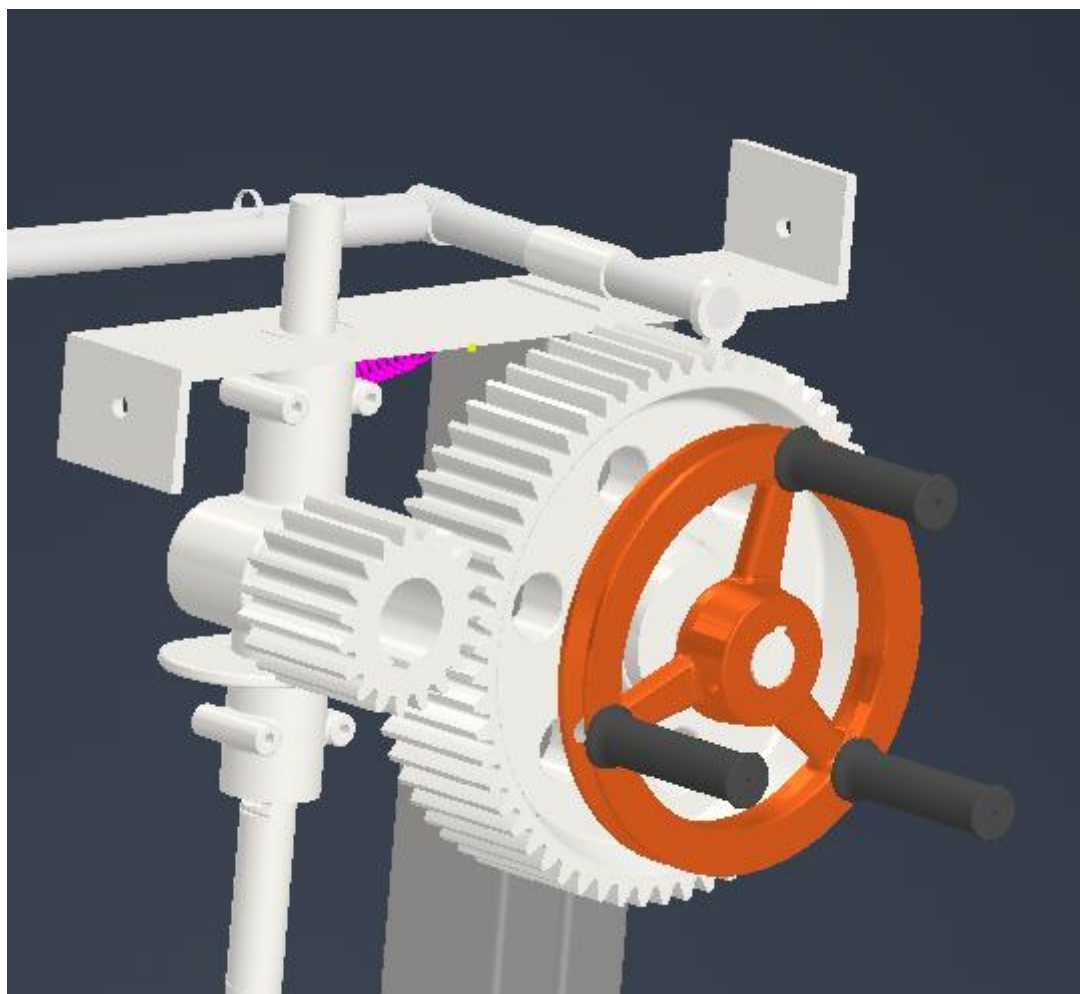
Sistema de engrenagens e setor de direção automotivo adaptado ao mecanismo de corte (Fonte: Própria)
